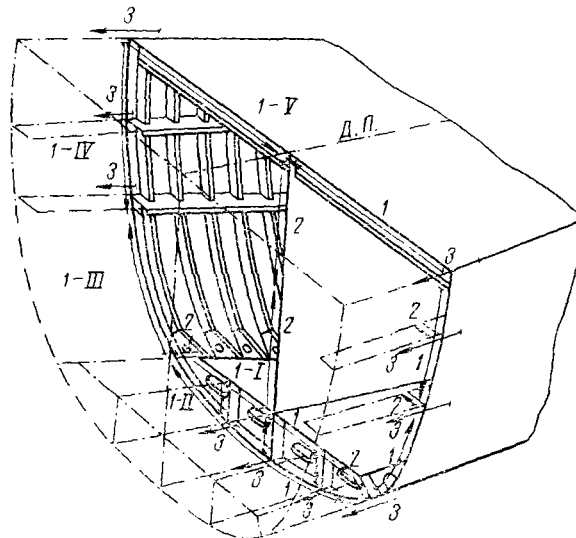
Схема порядка сварки межсекционного стыка блоков
